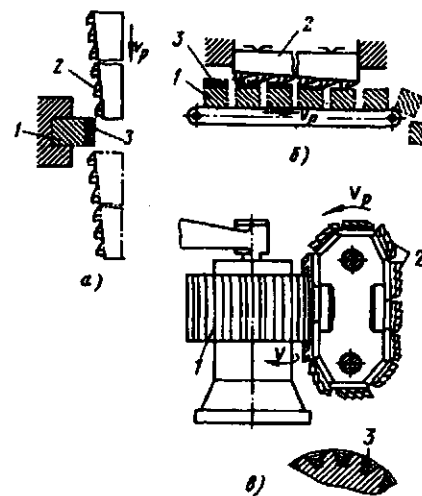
Виды наружного протягивания: 1 — деталь; 2 — протяжка; 3 — срезаемый слой металла; v_p — рабочий ход
